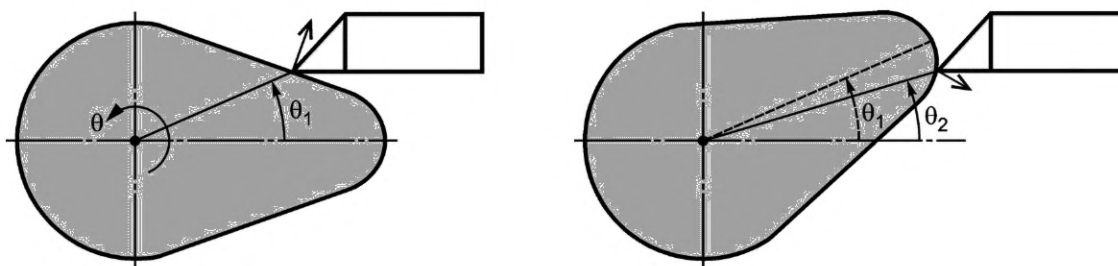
Изменяющееся чувствительное направление для операции токарной обработки
